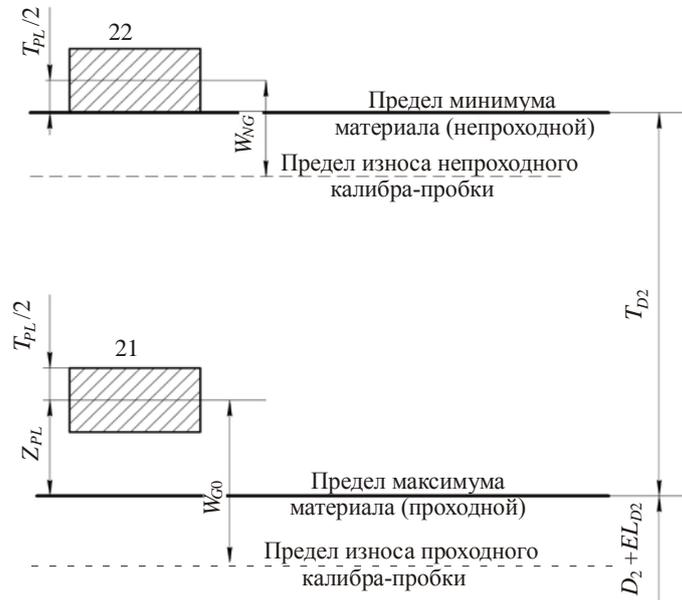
Расположение полей допусков среднего диаметра калибров для контроля внутренней метрической резьбы
